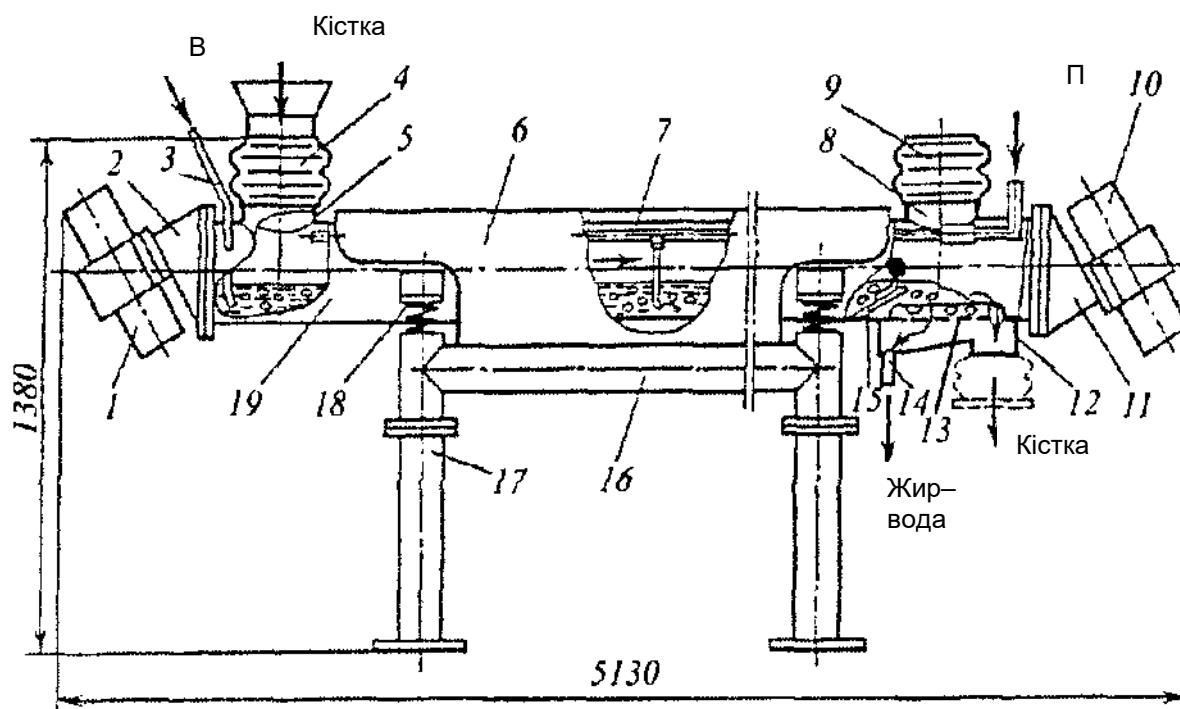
Вібраційний апарат ЕВГ-06: 1, 10 – вібратори; 2, 11 – кронштейни, 3 – патрубок для подачі води; 4, 9 – герметизатори; 5 – патрубок для завантаження кістки; 6 – захисний кожух; 7 – паровий колектор; 8 – вентиляційний патрубок; 12 – патрубок для вивантаження кістки; 13 – сітка; 14 – патрубок для відводу водожирової емульсії; 15 – заслінка; 16 – рама; 17 – стійка; 18 – пружини; 19 – корпус
